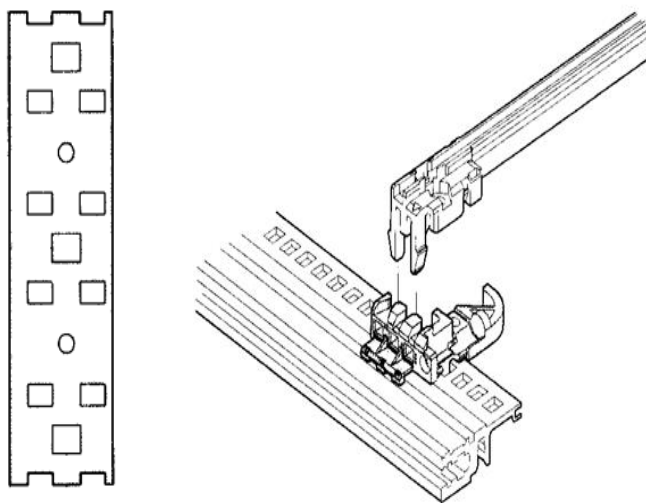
Примеры конструкций опорной планки (а) и кодировочного блока для субблока eucoras PRO немецкой компании Schroff (вертикальная опорная планка и горизонтальный профилированный рельс перфорированы) [48]
